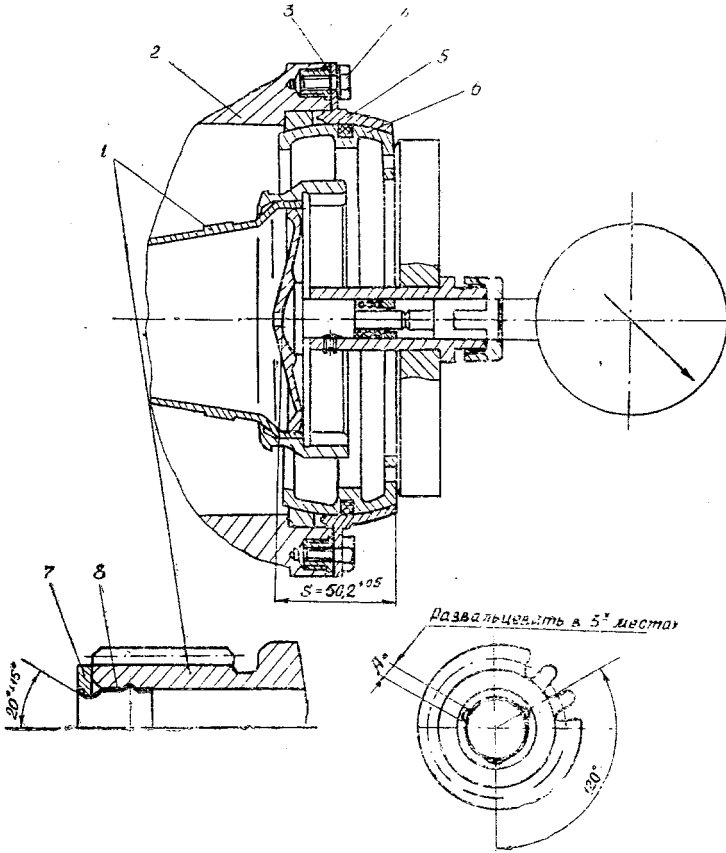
Схема замера утопания пружины главного привода и установки регулировочной шайбы:
